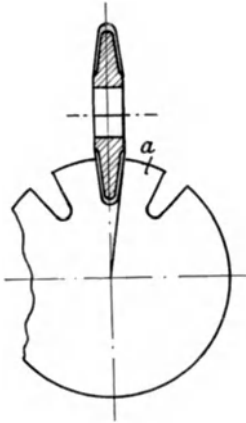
Das Fräsen der Nuten für hinterdrehte Fräser.
